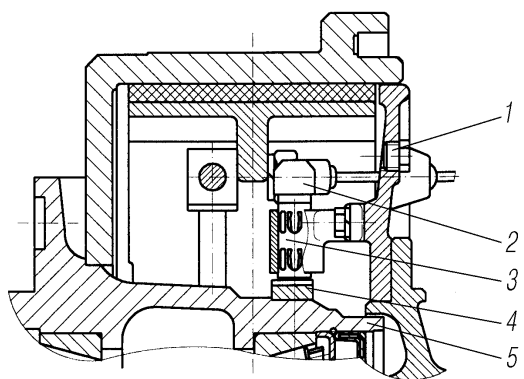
Механизм тормозной колесный: 1- пробка; 2- датчик индуктивный; 3- втулка зажимная; 4- кольцо импульсное зубчатое; 5- ступица колеса
